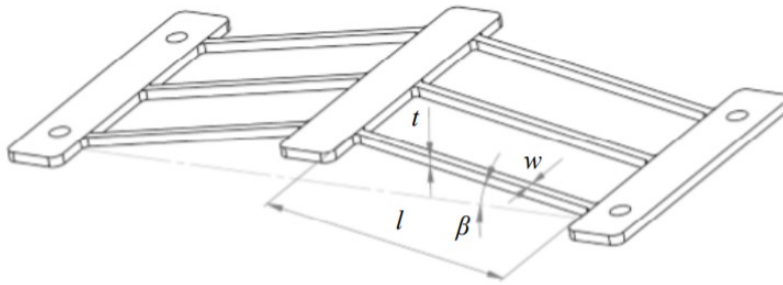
Parámetros geométricos de un actuador térmico con estructura de la viga en V [8].
